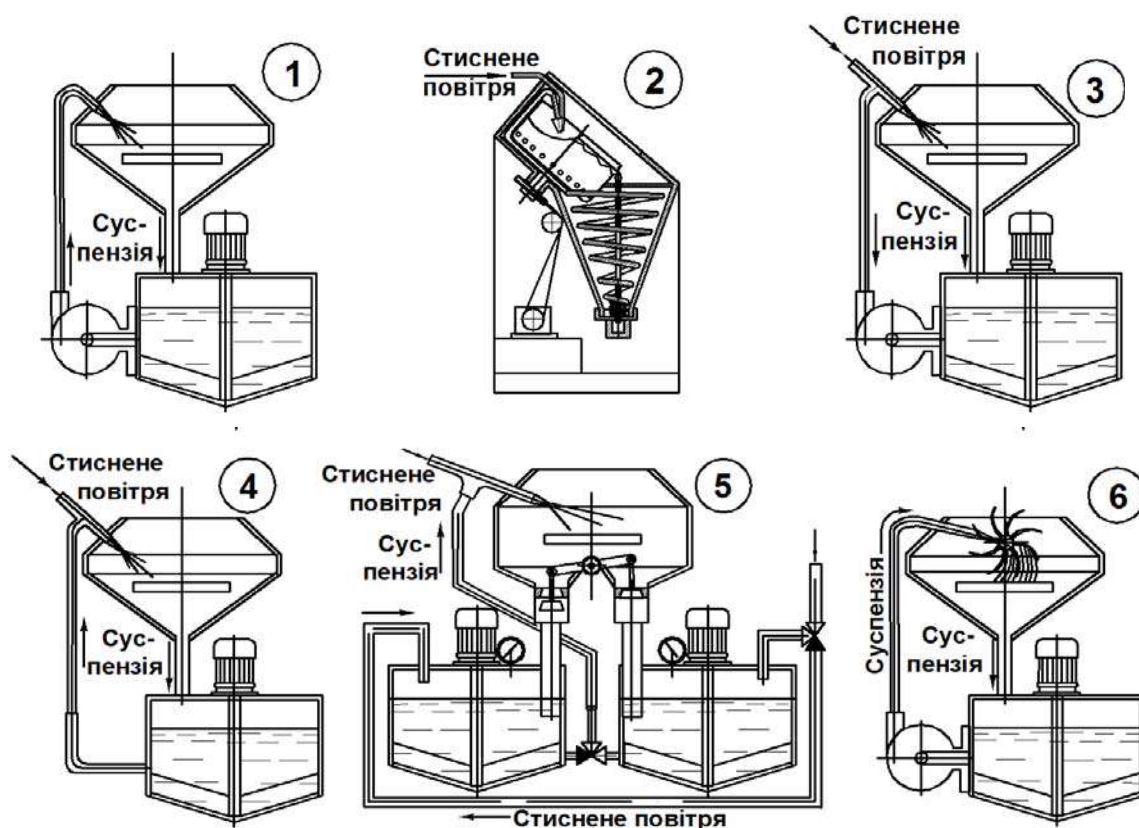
Струминні установки для обробки абразивною суспензією
